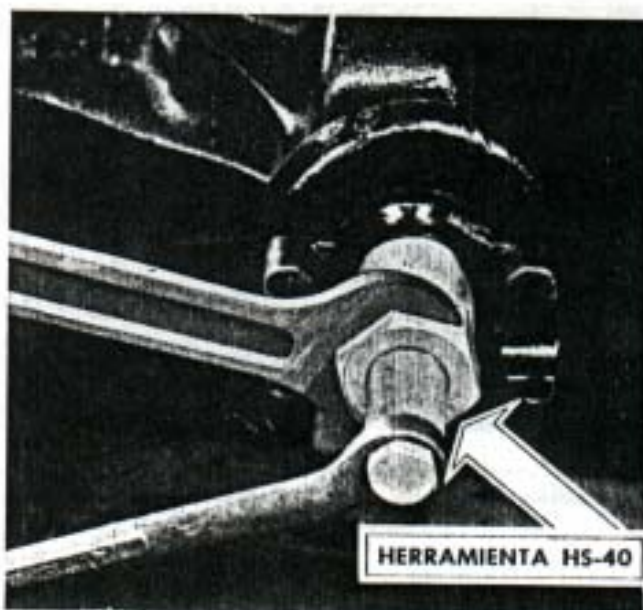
Instalando la horquilla de la junta universal con la herramienta HS-40.
